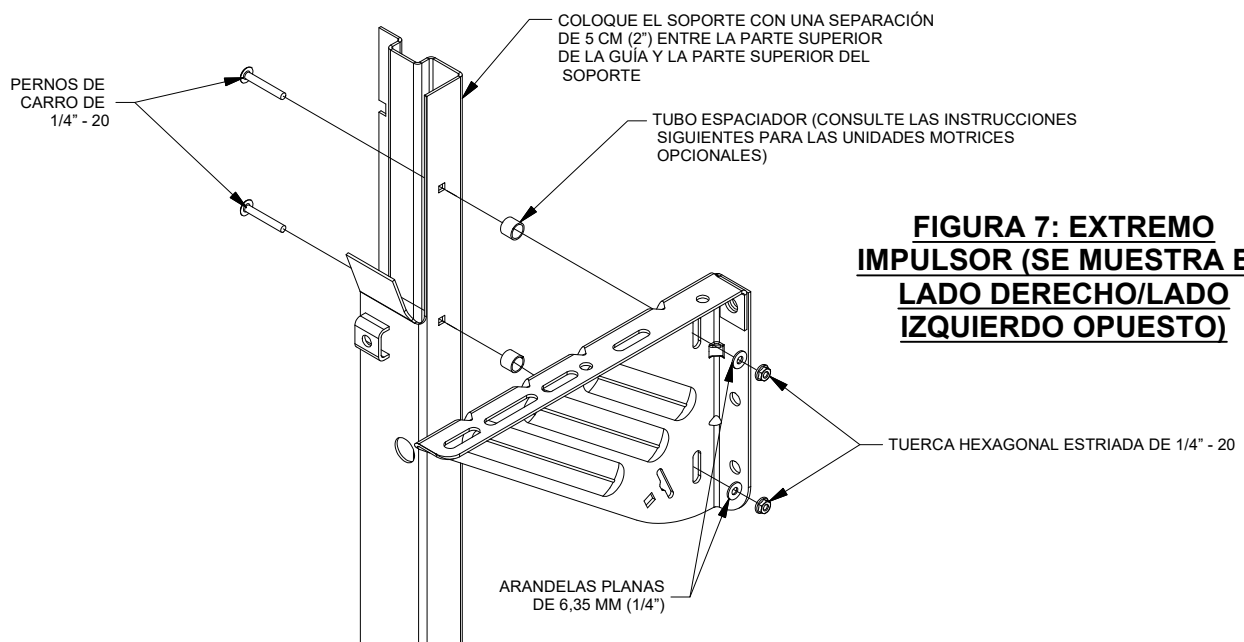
EXTREMO IMPULSOR (SE MUESTRA EL LADO DERECHO/LADO IZQUIERDO OPUESTO)
